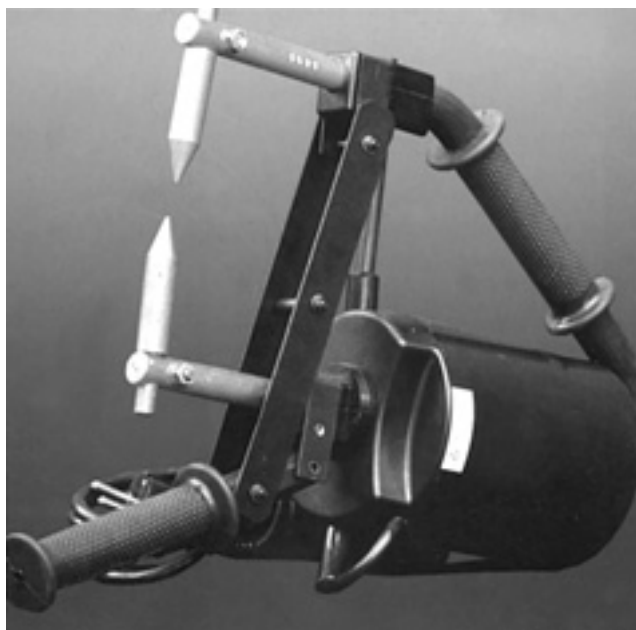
Аппарат для контактной сварки "ТОР"
